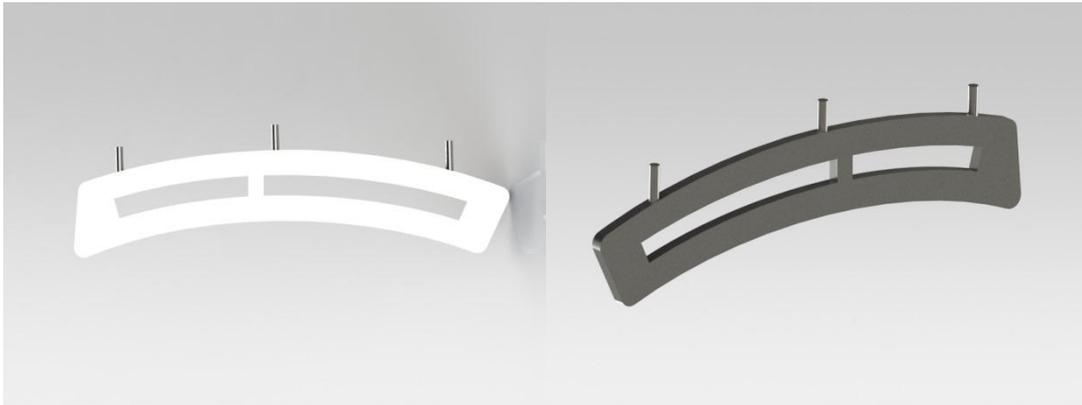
Vista in pianta e vista isometrica delle palette interiori
